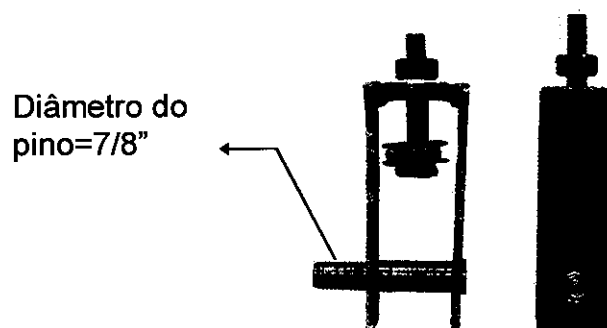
Dispositivo de fixação do corpo-de-prova à máquina de ensaio
